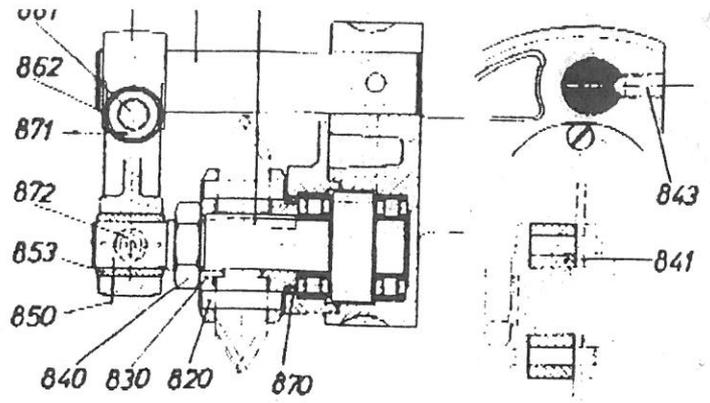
Fräserwelle mit Gegenhalter zu RBo 145-1a/RMO 5a
